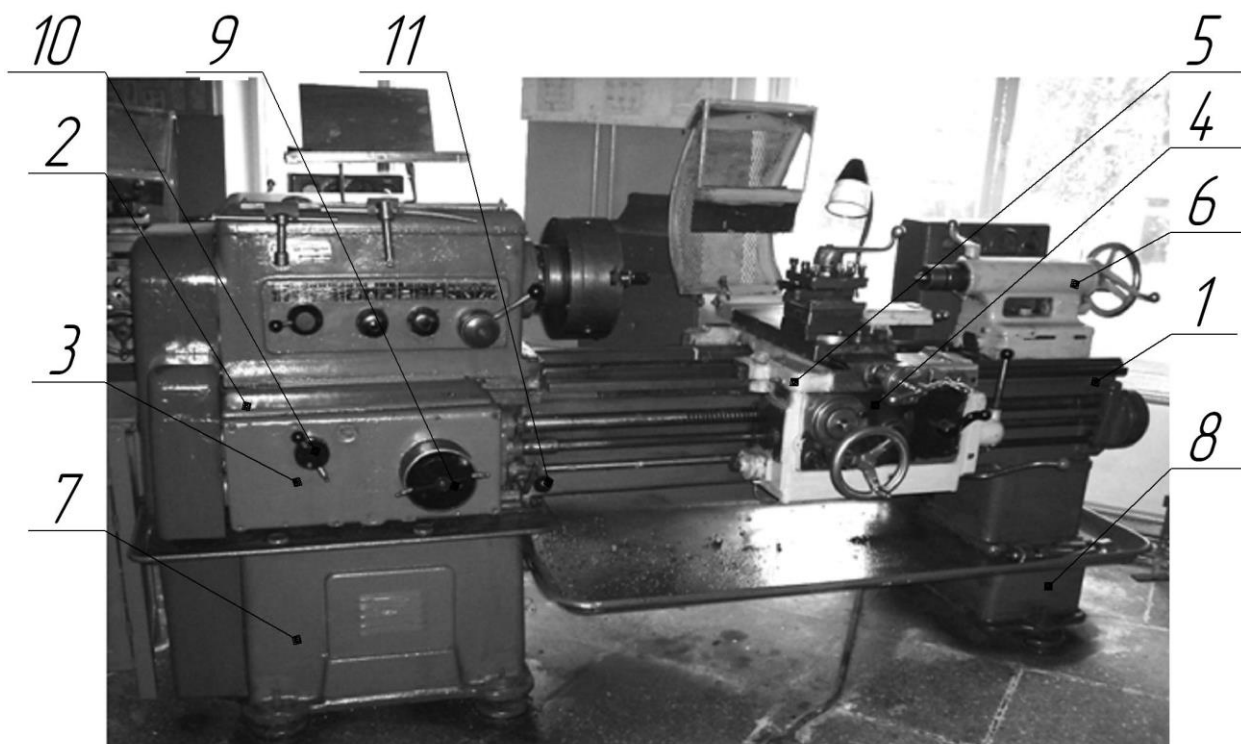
Общий вид станка: 1 – станина, 2 – передняя бабка, 3 – коробка подач, 4 – фартук, 5 – суппорт, 6 – задняя бабка, 7 – левая тумба, 8 – правая тумба, 9 – рукоятка выбора шага резьбы или подачи, 10 – рукоятка включения ходового винта напрямую и установка вида резьбы, 11 – рукоятка управления шпинделем
